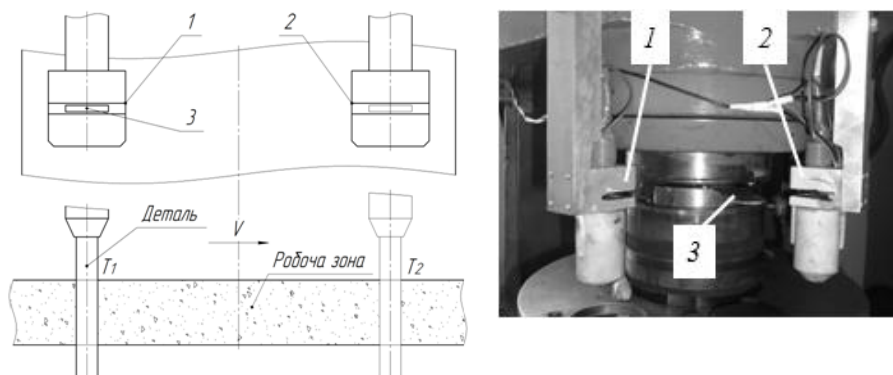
Схема вимірювання швидкості руху зразка вздовж робочої зони
